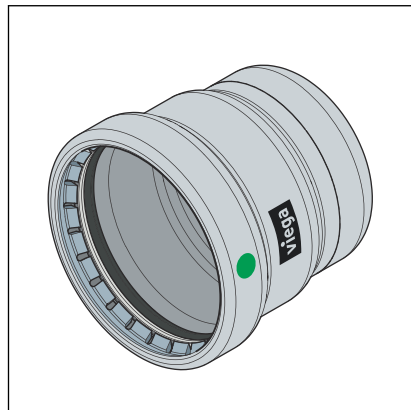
Megapress Stainless 316 XL-Pressverbinder
